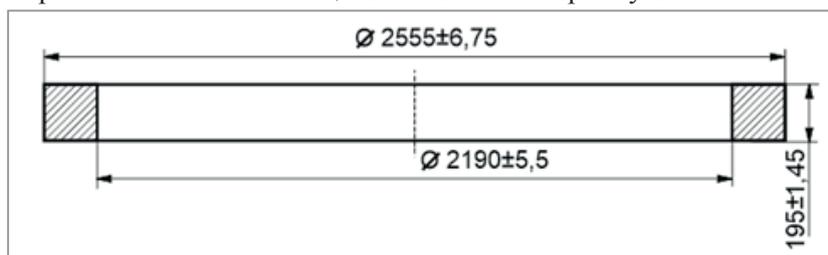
Эскиз окончательной кольцевой заготовки с прямоугольным сечением
